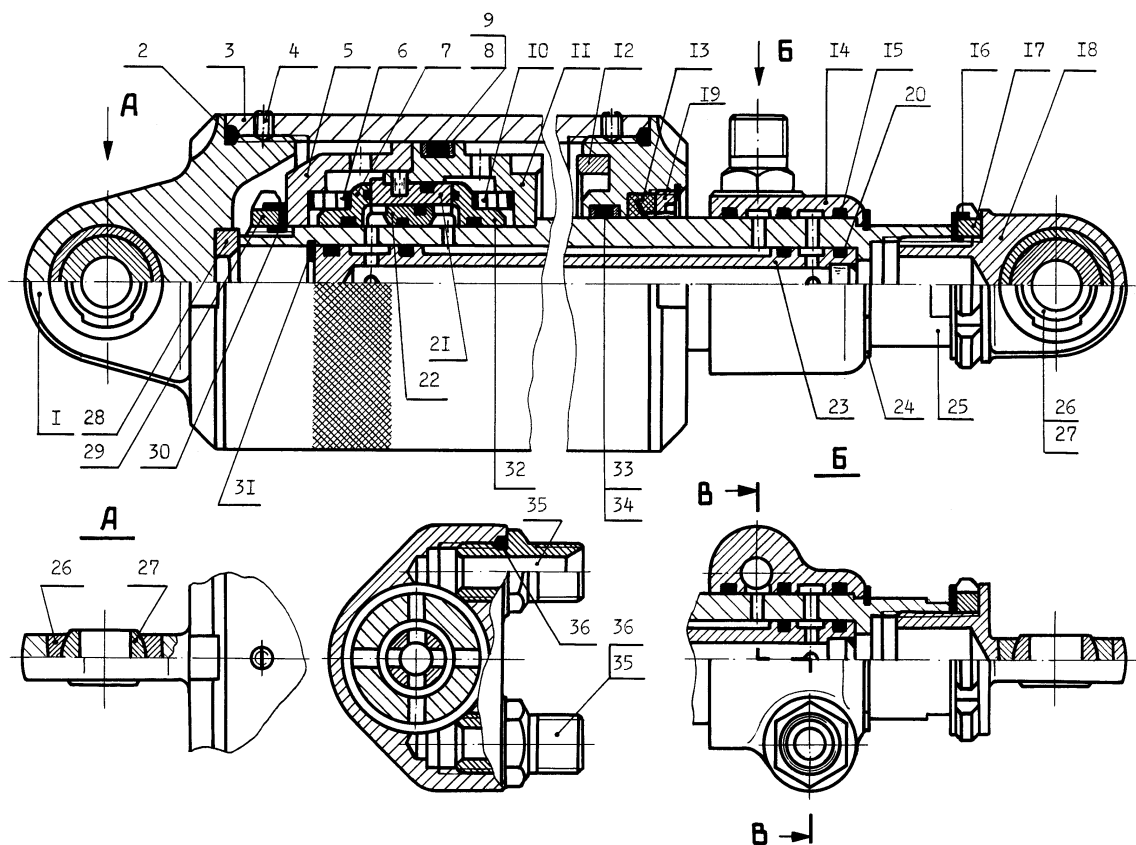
Конструкция гидроцилиндра ЭгСП/Д: 1 – задняя крышка; 2, 8, 15, 33, 36 – кольца уплотнительные; 3 – корпус; 4 – винт контрольный; 5 – крышка поршня; 6, 10 – пружина; 7, 32 – тарельчатый ЗРЭ гидрозамка; 9, 34 – кольцо защитное; 11 – поршень; 12, 28 – кольцо упорное; 13 – грязесъёмник; 14 – корпус коллектора; 16, 30 – шайба; 17, 29 – гайка; 18 – проушина; 19 – гайка грязесъёмника; 20 – заглушка; 21 – корпус гидрозамка; 22 – толкатель; 23 – трубка; 24, 31 – кольцо пружинное; 25 – шток; 26 – втулка; 27 – втулка сферическая; 35 – штуцер.
